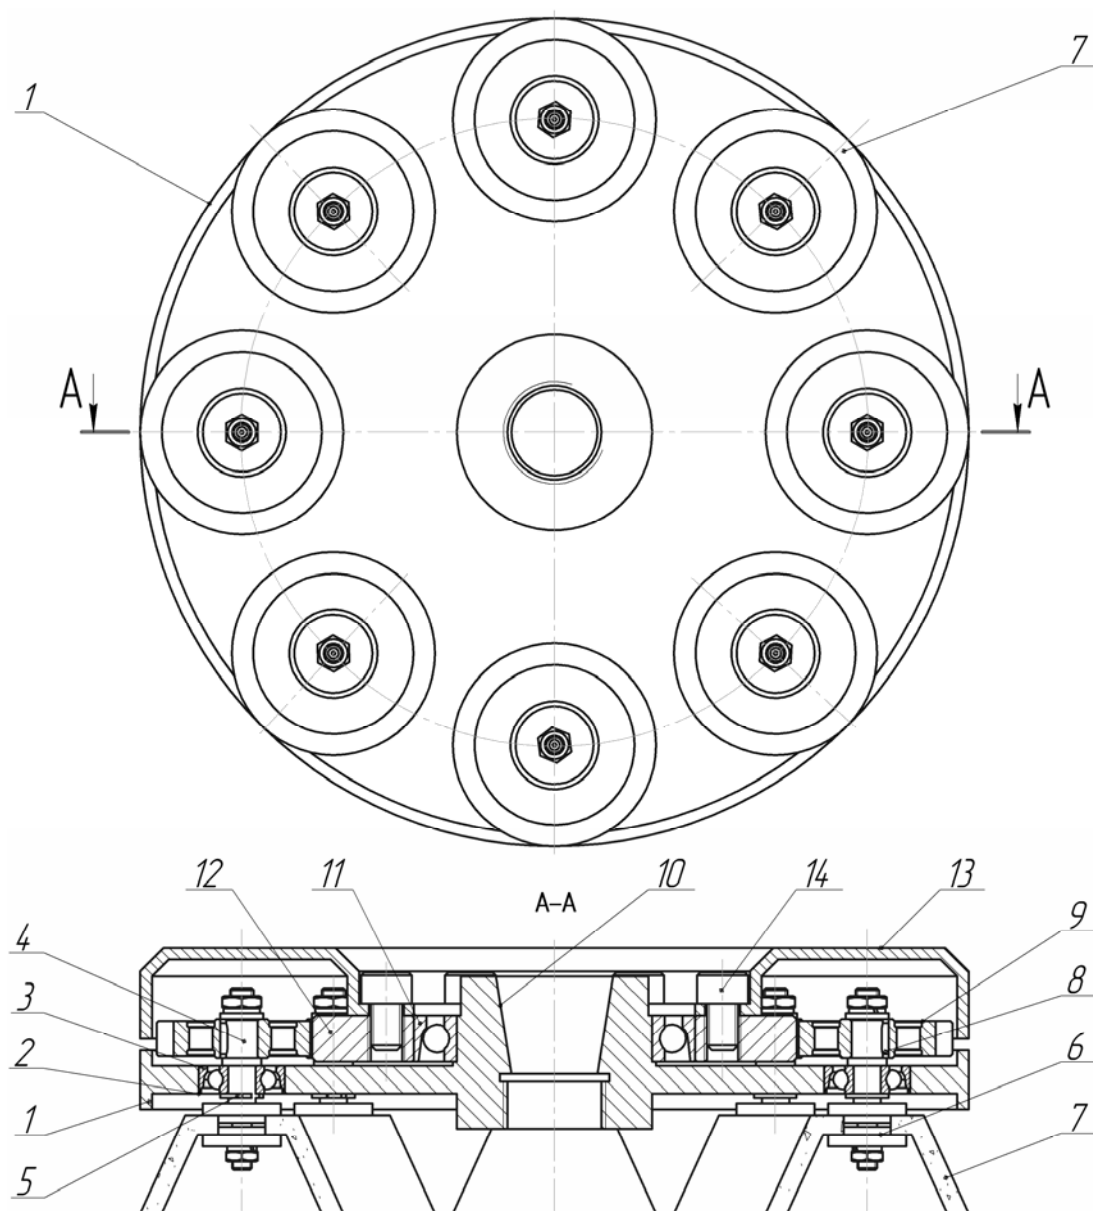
Багаточашковий абразивний інструмент з приводними чашками
